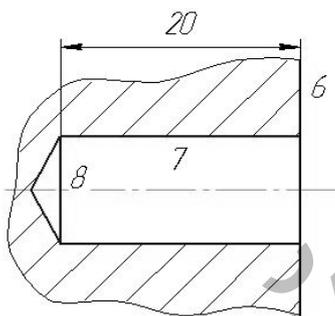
Центровое отверстие, выполненное в торцевой поверхности вала
